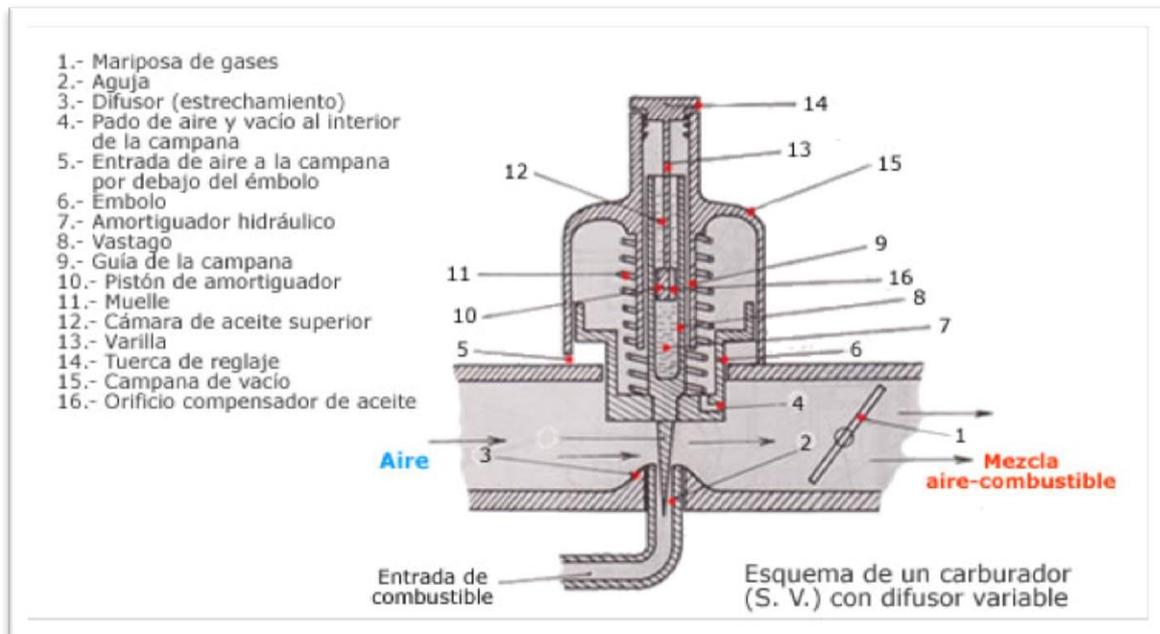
Partes que constituyen un carburador con difusor variable / Fuente: www.todomotores.cl
